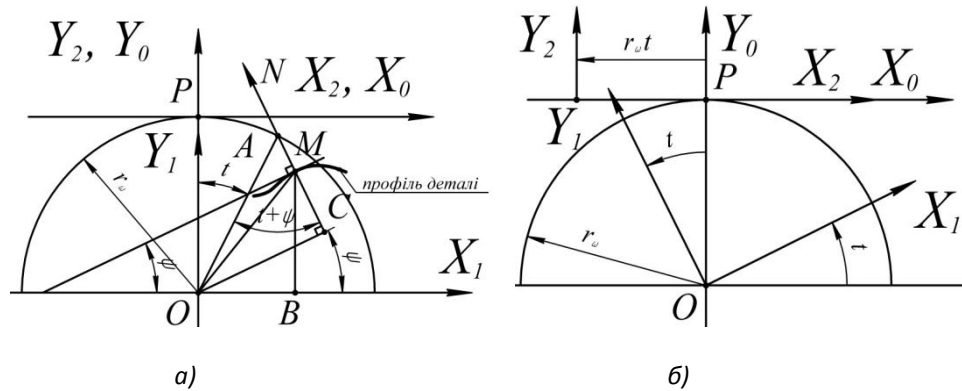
Схема формоутворення при коченні початкового кола деталі по початковій прямій інструмента
